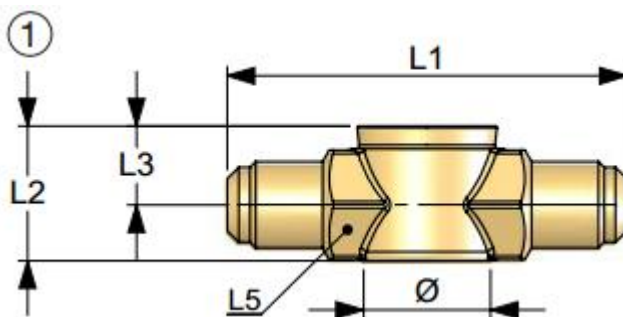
Dimensiones de la mirilla Carly VCYL 13
